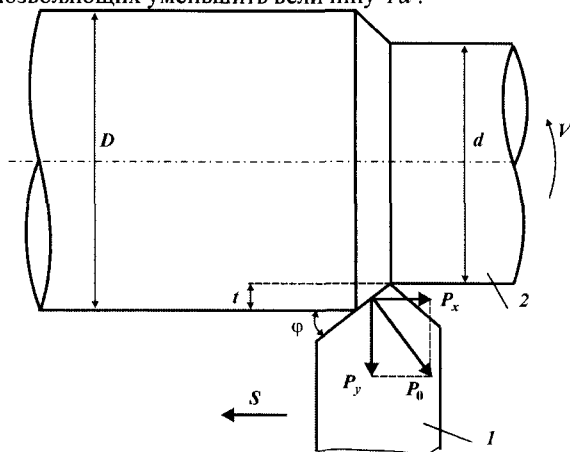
Расчетная схема продольного точения: 1 – резец; 2 – обрабатываемая деталь.
